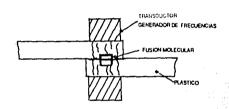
Soldadura ultrasonica. (Ref. 8).
